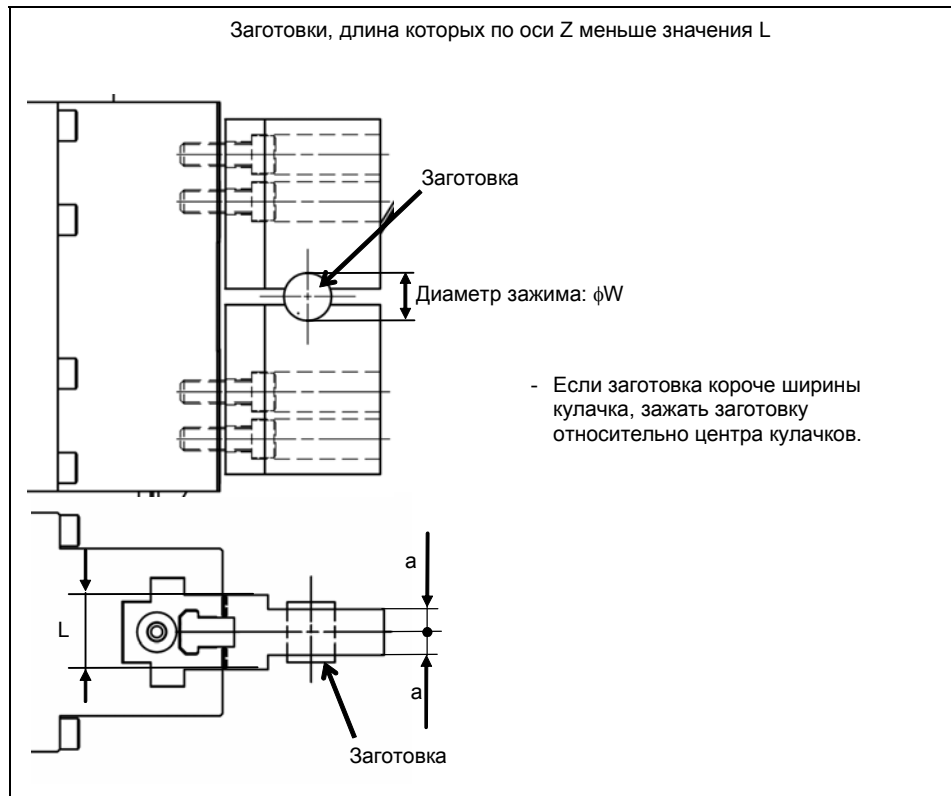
Обработка мягких кулачков (зажим заготовки по наружному диаметру 2)
